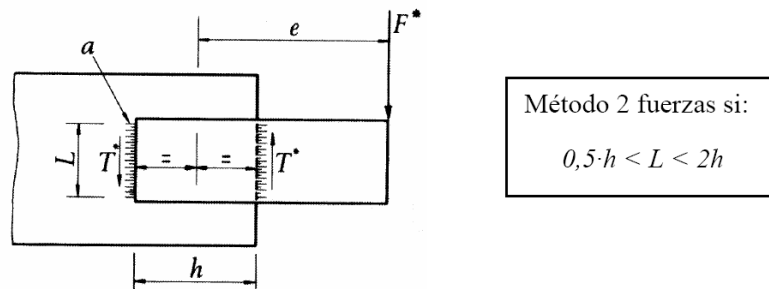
SOLDADURAS FRONTALES SOMETIDAS A TORSIÓN Y CORTANTE
